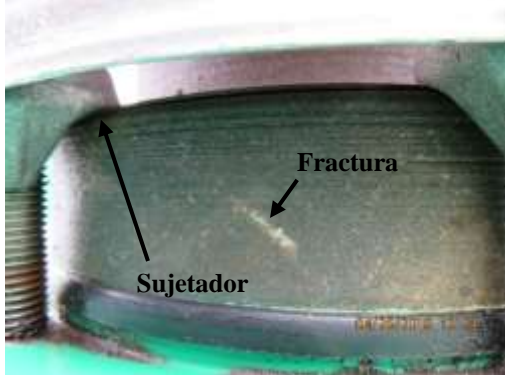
Detalle de fractura en borne Y2 fase “C”.
